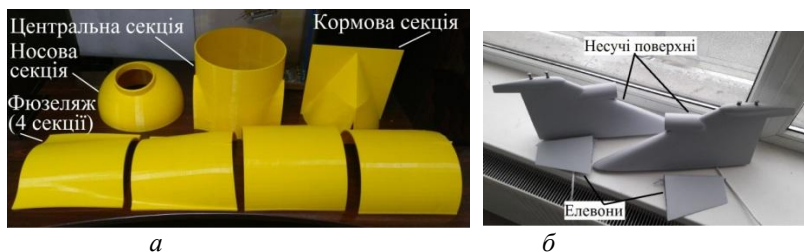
Виготовлені за допомогою 3D-принтера елементи легкого корпусу (а), несучих поверхонь та елевонів БПА проекту «Глайдер» (б)
